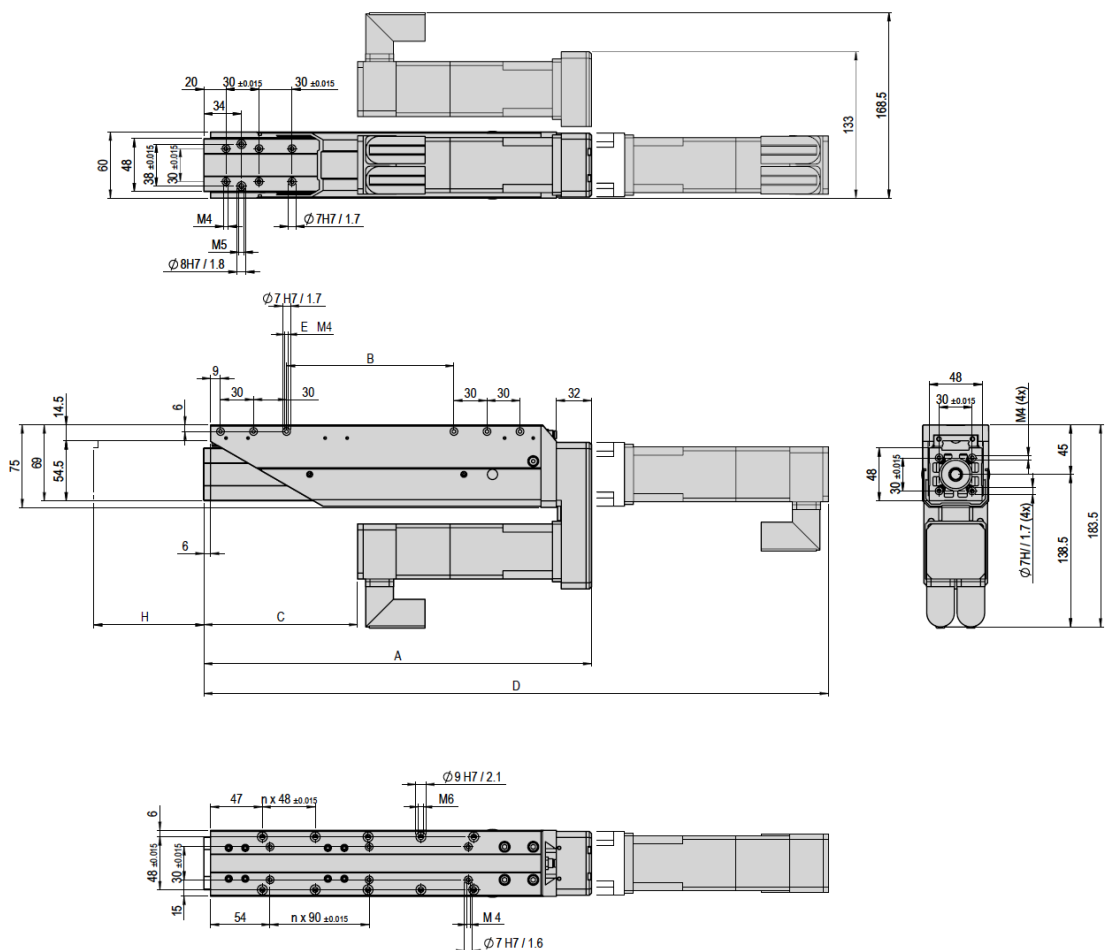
Masszeichnung Spindelausleger SA-6 und SA-6-FL
